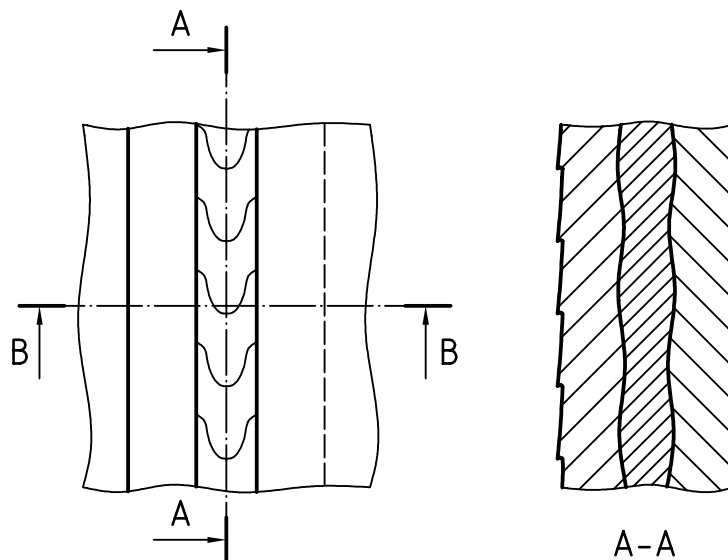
Positions recommandées pour prélever des sections dans des éprouvettes: soudures à la molette
